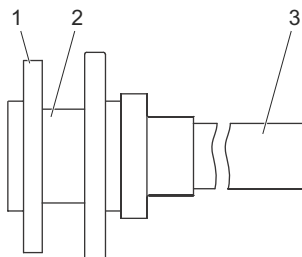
Стандартный инжекционный клапан до 4000 л/ч
